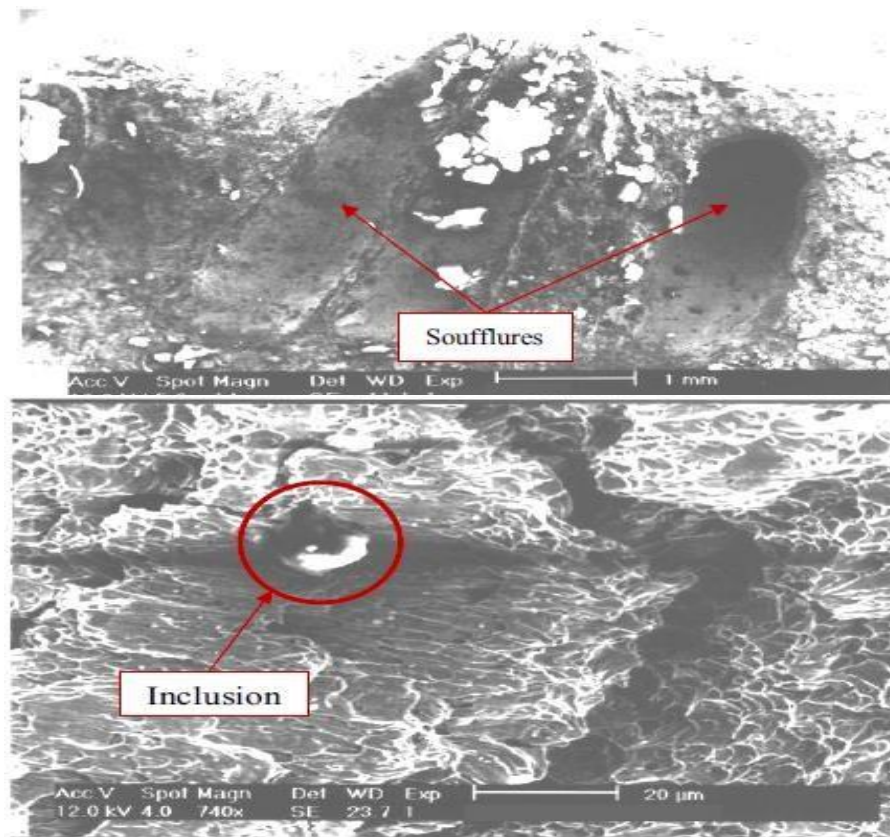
8: Soufflures et inclusions dans les soudures.
